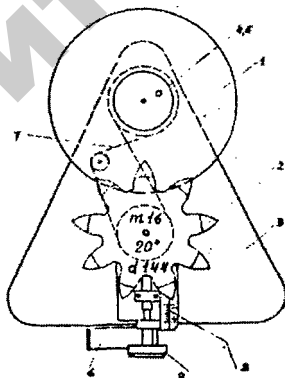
Схема прибора для нарезания зубчатых колес долбяком:
